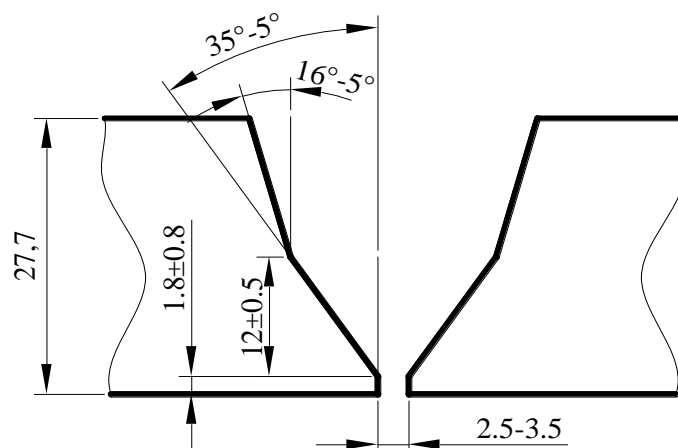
Подготовка кромок труб под сварку
